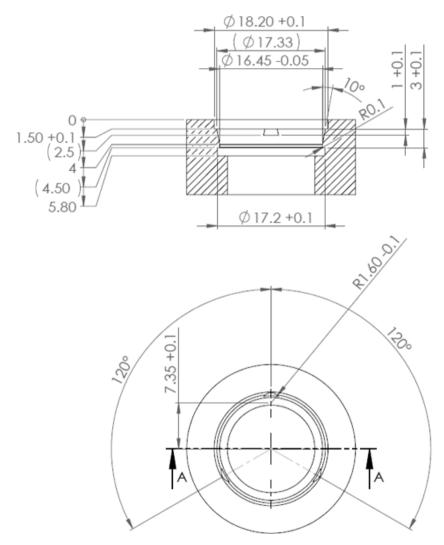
Desenho de dimensões: Furo da peça para montagem da variante especial do MDS D522
